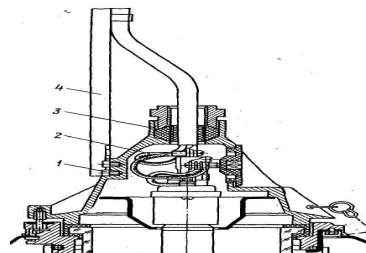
Промисловий світильник: 1 – болти кріплення монтажного профілю до корпусу; 2 – жили кабелю; 3 – гумове ущільнювальне кільце; 4 – монтажний профіль
